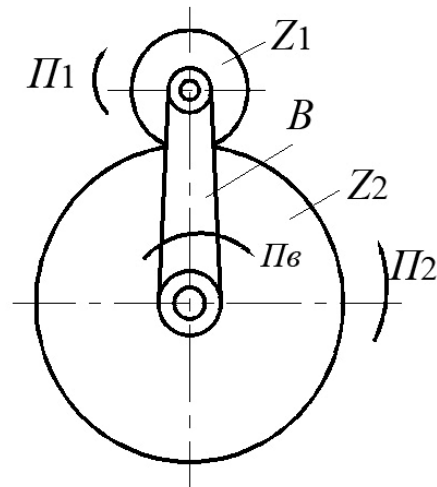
Планетарный суммирующий механизм с цилиндрическими колесами
